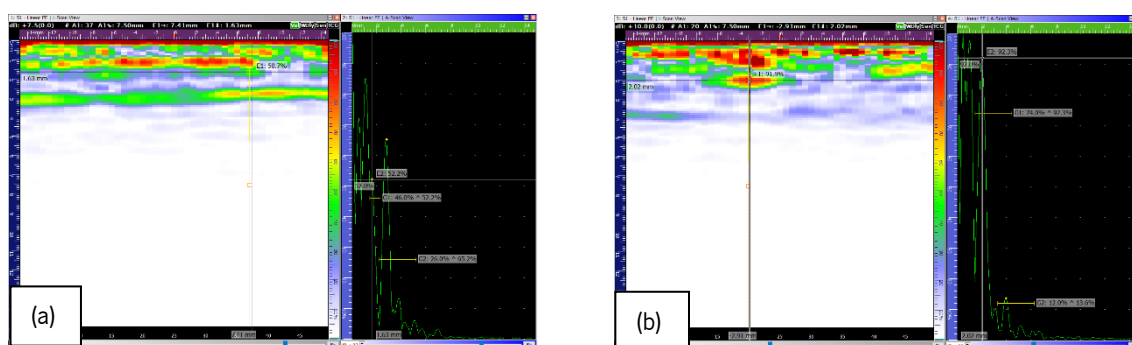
(a) Inclusão de alumínio de dimensões 3×3 mm² colocada na zona de espessura 3,13 mm; (b) inclusão de alumínio de dimensões 7×7 mm² colocada na zona de espessura 4,04 mm.
